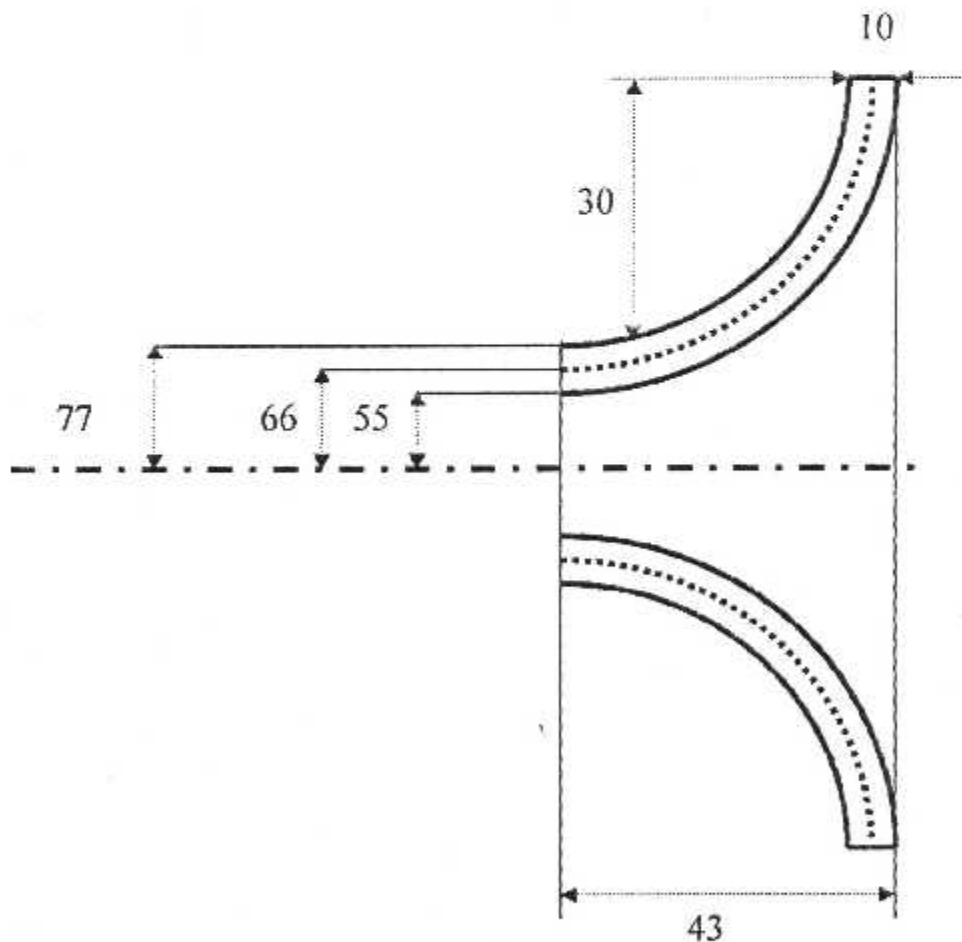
Dimensions de la rouet du compresseur centrifuge
